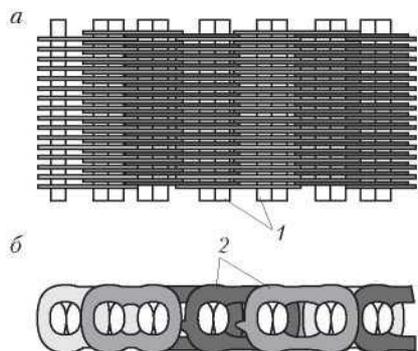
Вариаторная цепь: а — вид сверху; б — вид сбоку; 1 - соединительные оси; 2 — звенья
